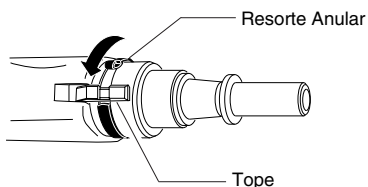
Inserción del conjunto cañón en el conjunto forro exterior
